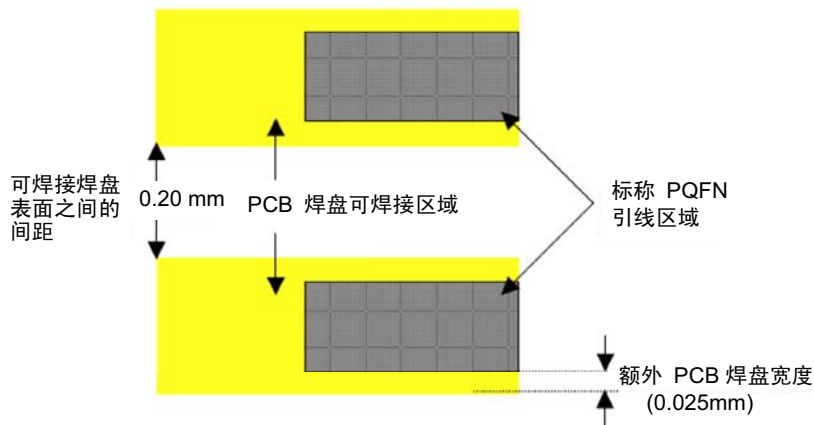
PCB 顶视图和 PQFN 引脚的推荐 PCB 焊盘尺寸
